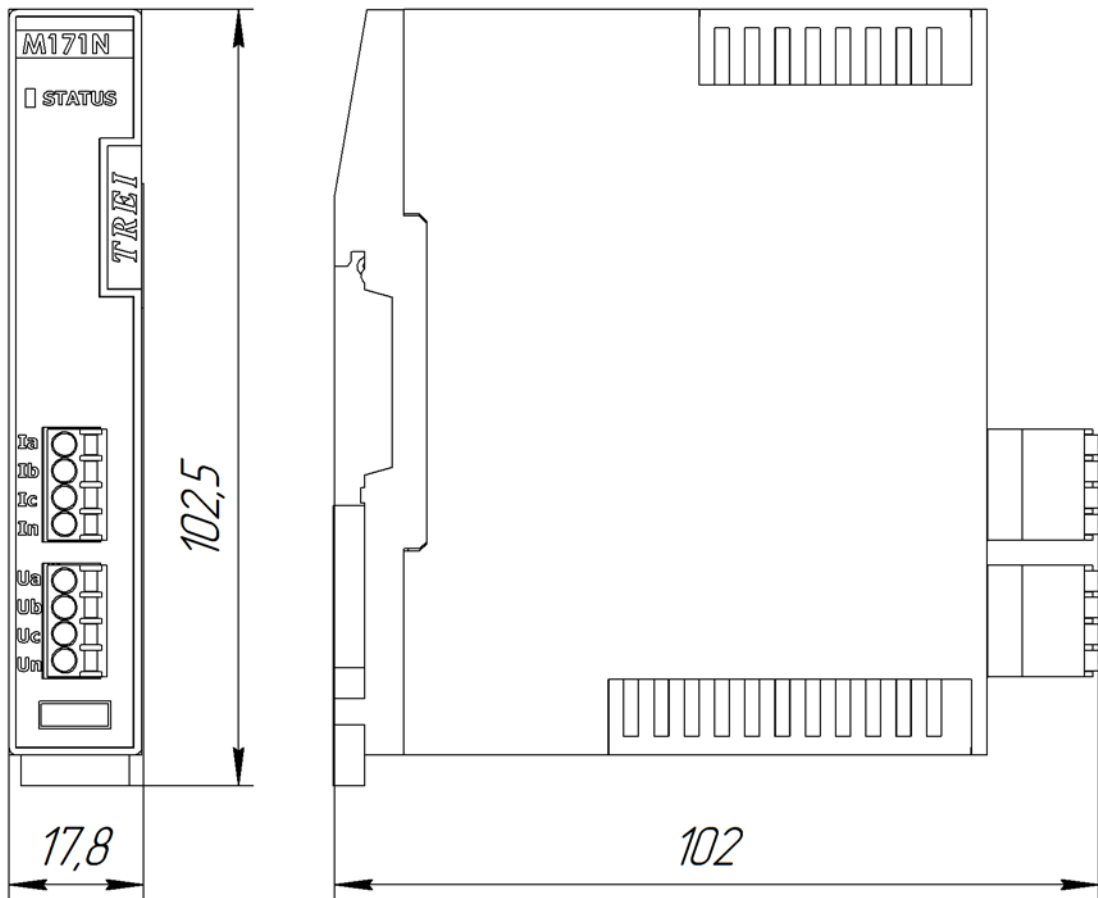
Чертеж общего вида M171N с указанием габаритных и присоединительных размеров
